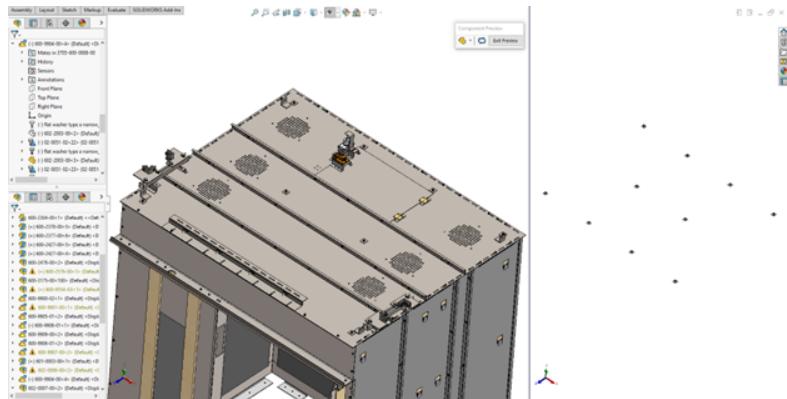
Tambié se puede utilizar en el subensamble de los bolt packs para seleccionar cada uno sin problema
